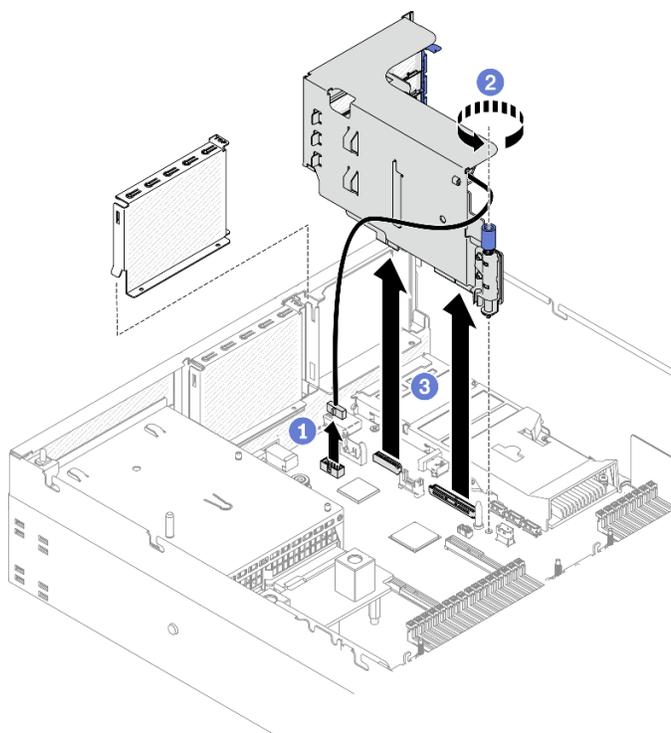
Removendo a placa riser PCIe 1 instalada com porta serial
